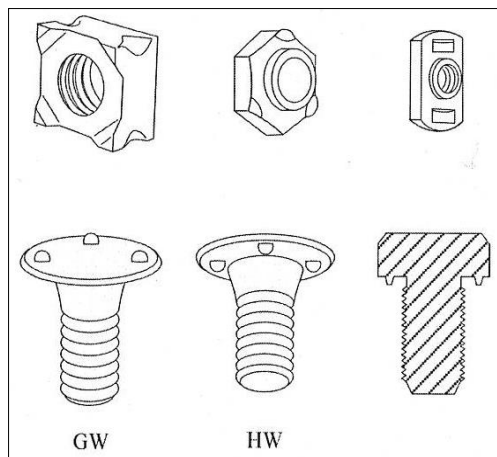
Forma de tuercas y tornillos aptos para la soldadura por proyección.
